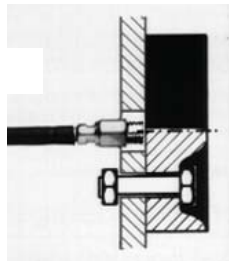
Geschirmter Sensor mit Gewinde in Standardmontage
